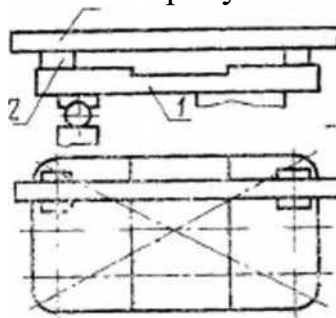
Схема проверки плоскостности рабочей поверхности шипорезной каретки
